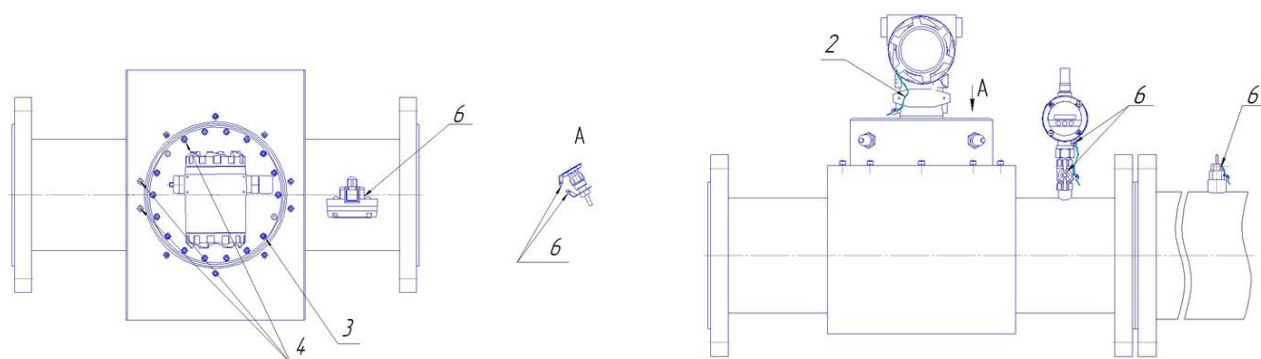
Корпус круглого сечения с защитным кожухом
